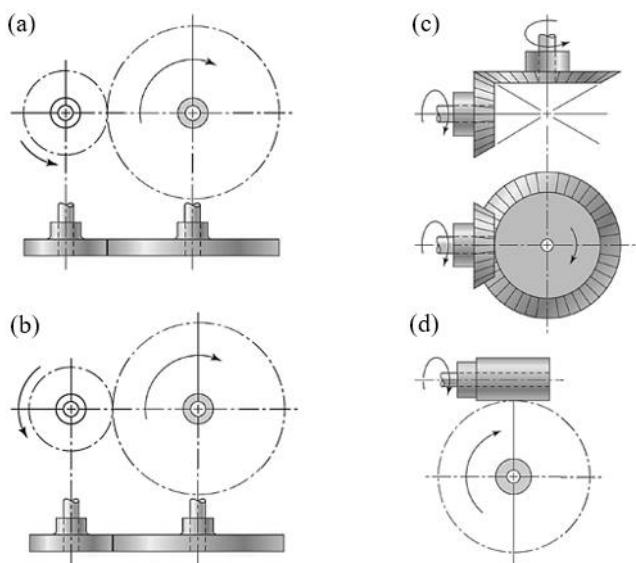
Engrenagens do tipo (a) cilíndrica de dentes retos, (b) helicoidais, (c) cónicas e (d) sem-fim [3].
